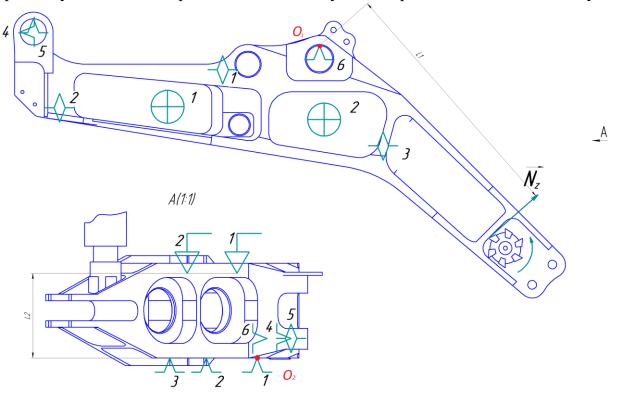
Схема закріплення заготовки При розташуванні зуба фрези в точці В горизонтальна сила прагне розвернути заготівлю відносно точки О $_1$, створюючи момент, рівний $M=P_z*l$
